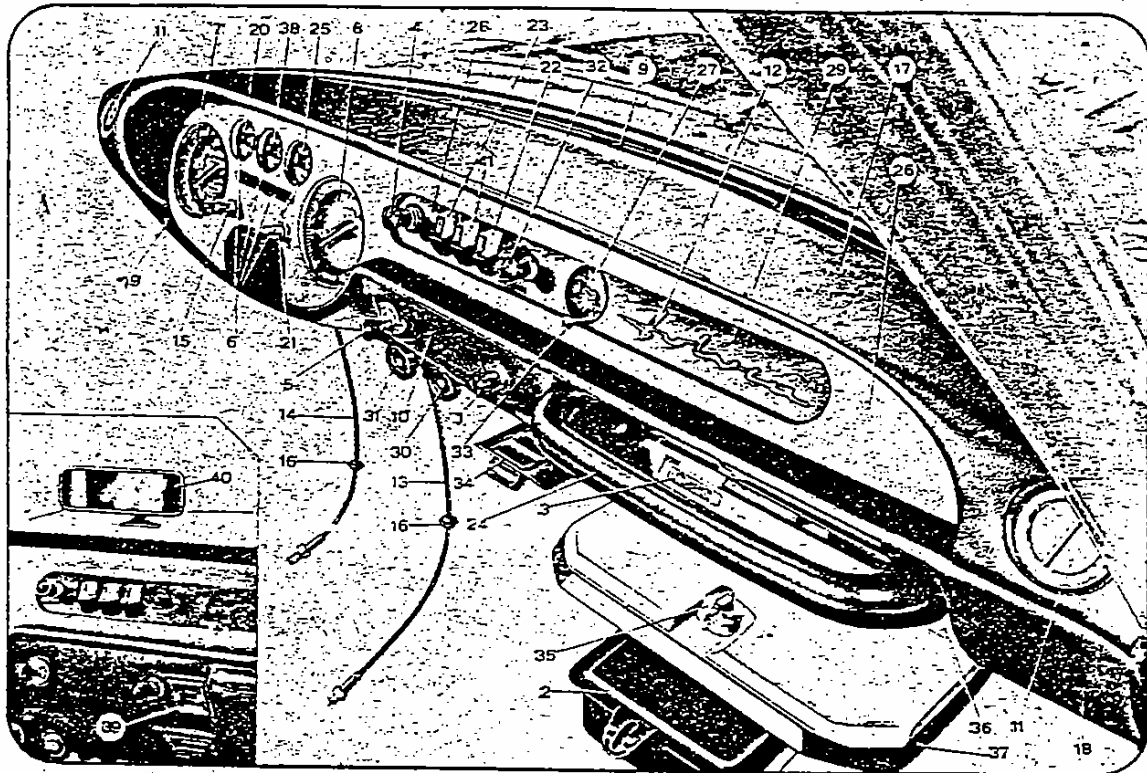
/004 - Equipement planche de bord (Du Catalogue Pièces Détachées)
